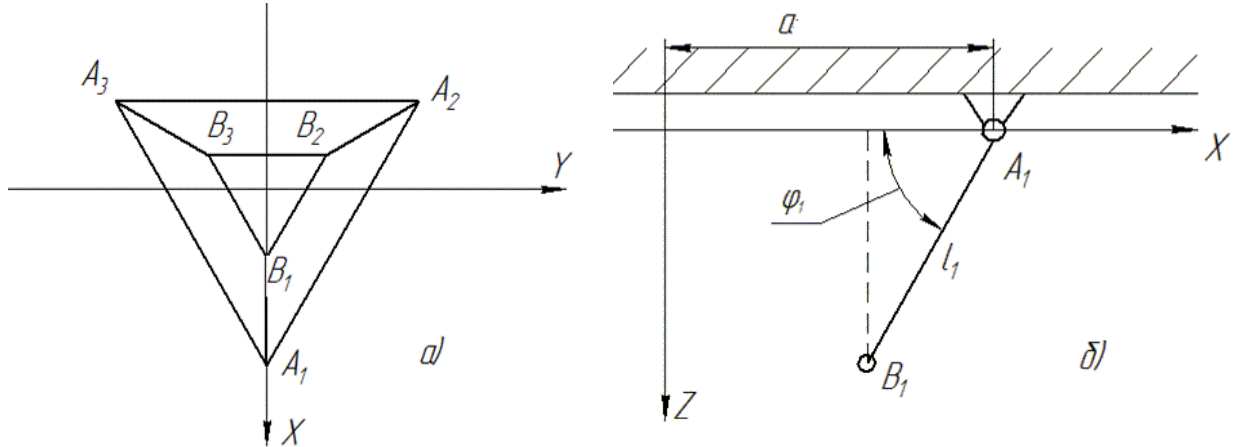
Розрахункові схеми (а – схема механізму вид зверху, б – схема сполучення штанги з основою)
